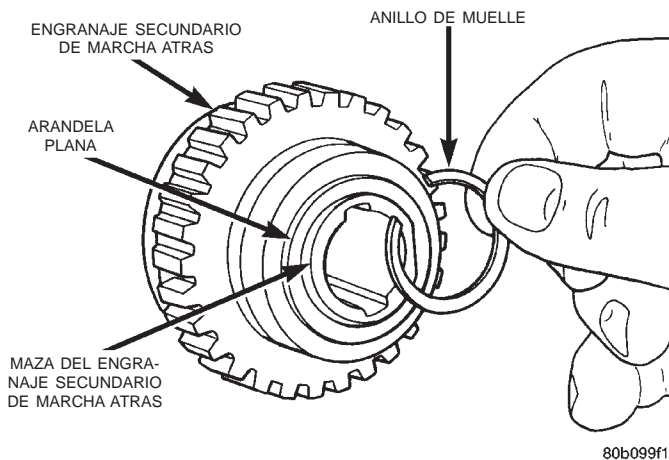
Desmontaje del anillo de muelle del engranaje secundario de marcha atrás
